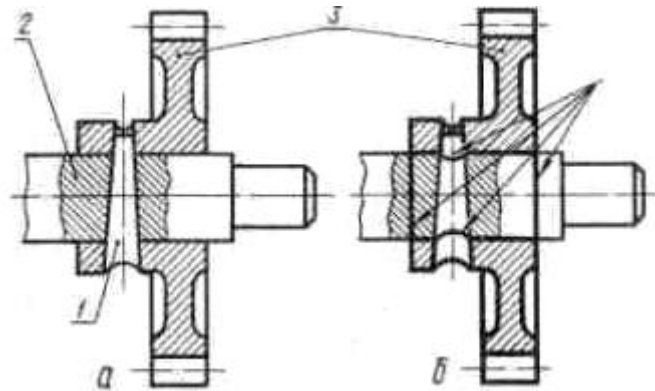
Читання креслення деталі, внутрішні контури якої закриті іншою деталлю
